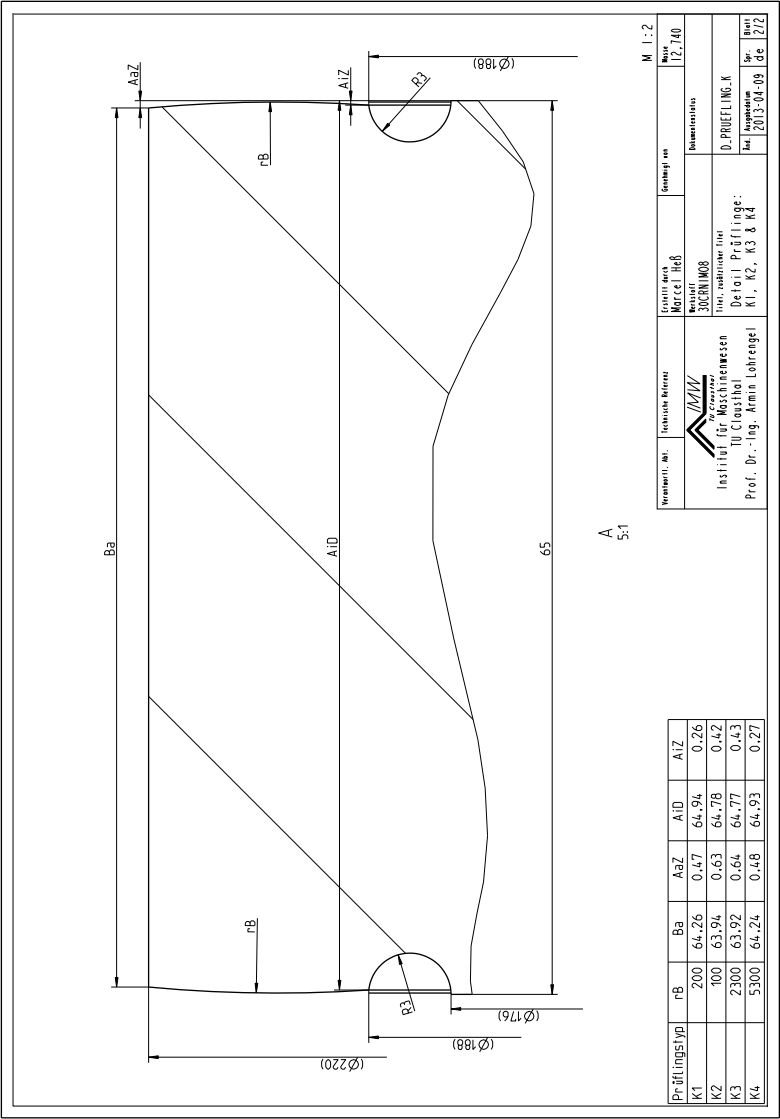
Detailzeichnung für Prüflinge des Typs A: Prüflingsgeometrie mit ebenen Laufflächen und verrundeten Außenkanten.
